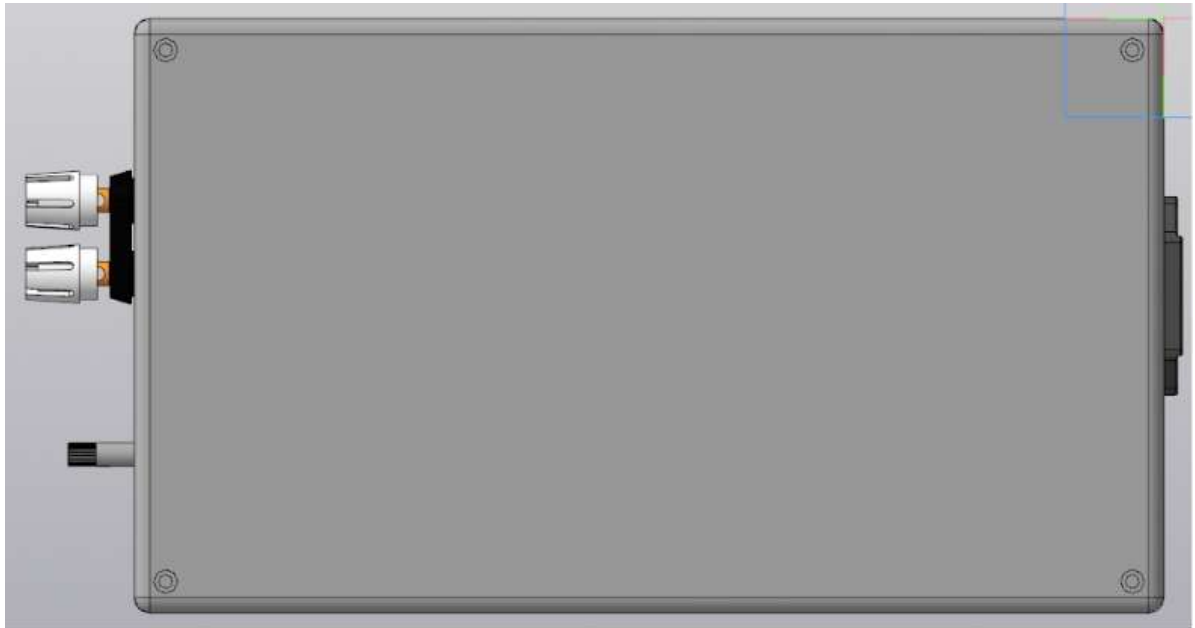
3D модель пристрою в корпусі, вид зверху
